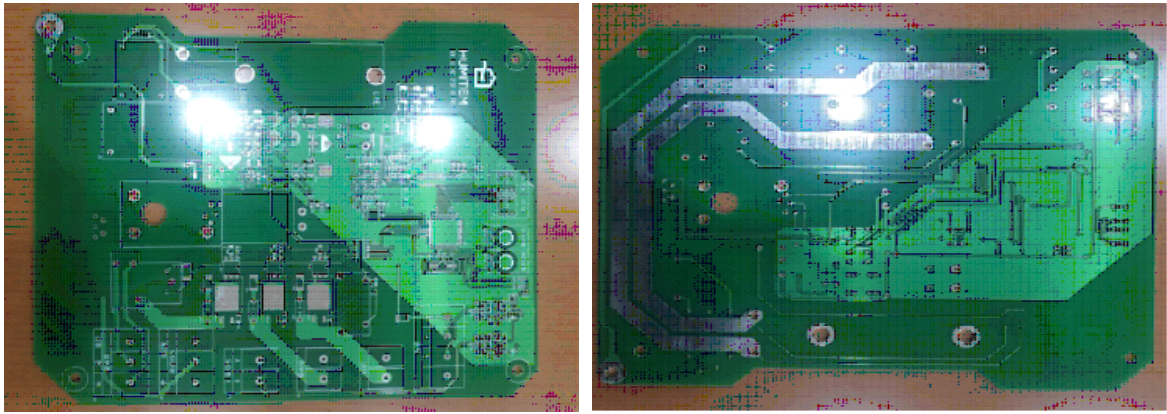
정밀 공조기 제어 PCB 설계 및 제작 (1)
